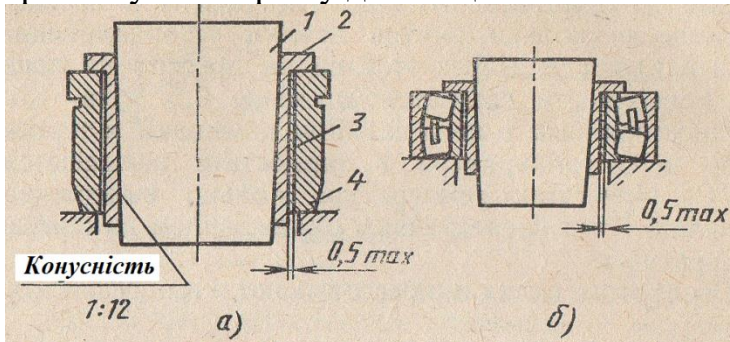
Пристосування для приклеювання сталюї стрічки на підшипники
